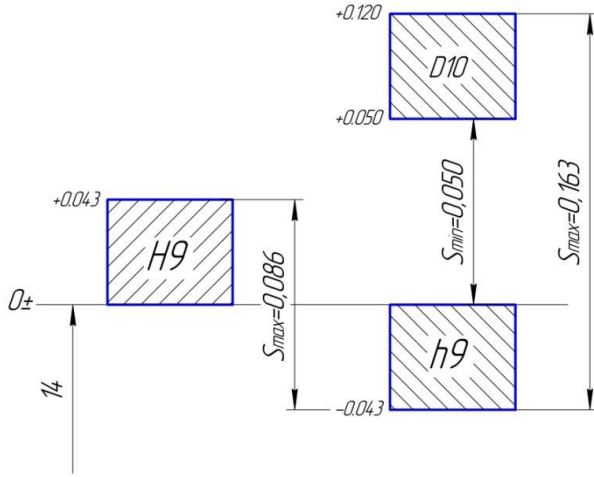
Схема розташування полів допусків шпонкового з'єднання
